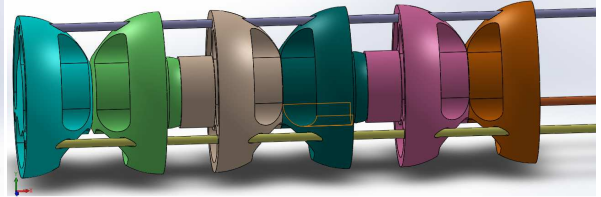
Sfere cu parte cilindrică - 3 tije
